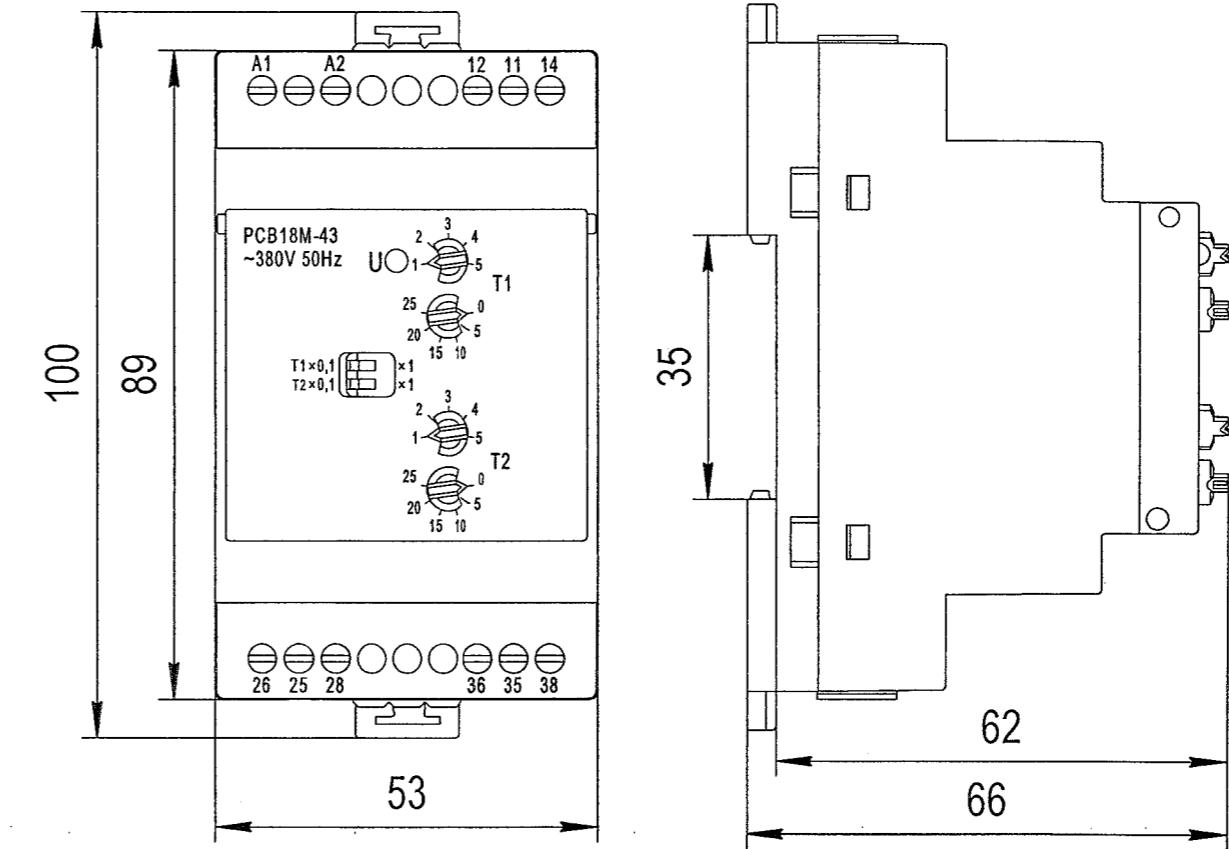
Реле типов PCB18M-XX-XX-XXX4
